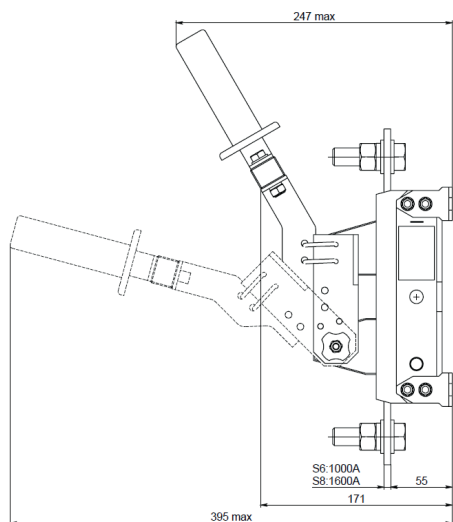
Разъединитель РЕ19 с центральным рычагом для управления штангой
